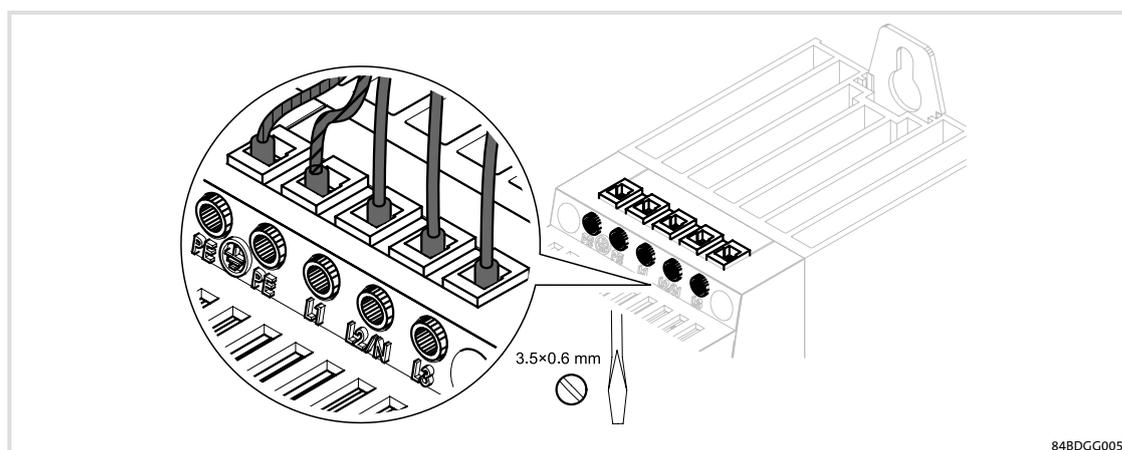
Collegamento lato rete del dispositivo alla terra di protezione
